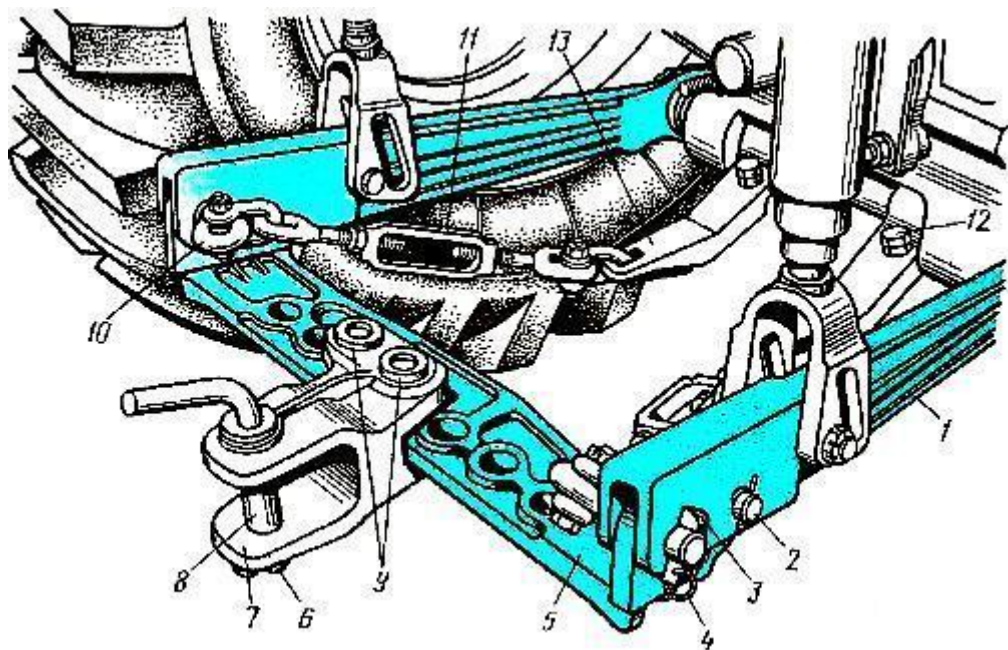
Зовнішній вигляд конструкції причіпного пристрою трактора: 1 – передній кінець поздовжньої тяги; 2 і 9 – пальці; 3 – чека; 4 – пружинне кільце; 5 – поперечина; 6 – пружинний шплінт; 7 – причіпна вилка; 8 – шворінь; 10 – вушко; 11 – стяжка; 12 – регульовальні болти; 13 – кронштейн
